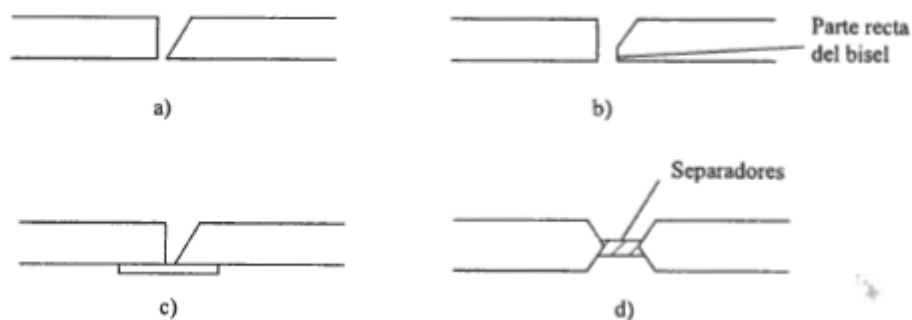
Preparación de los bordes para soldadura de ranura.
